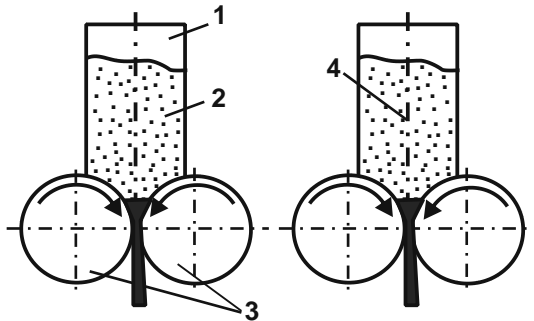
Схема листового прокатування одношарових та двошарових порошоків: 1 – контейнер; 2 – порошок; 3 – вальці; 4 – перегородка
